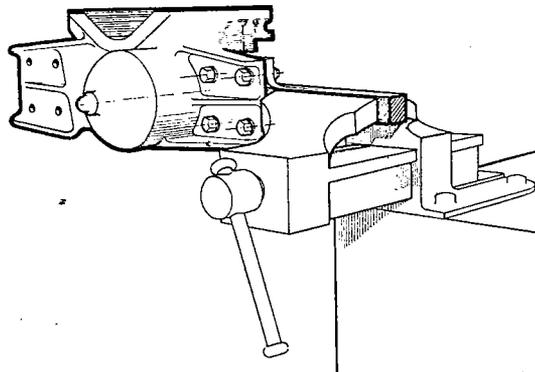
FIXATION DU CARTER ARRIÈRE DANS L'ÉTAU (8° VUE)
